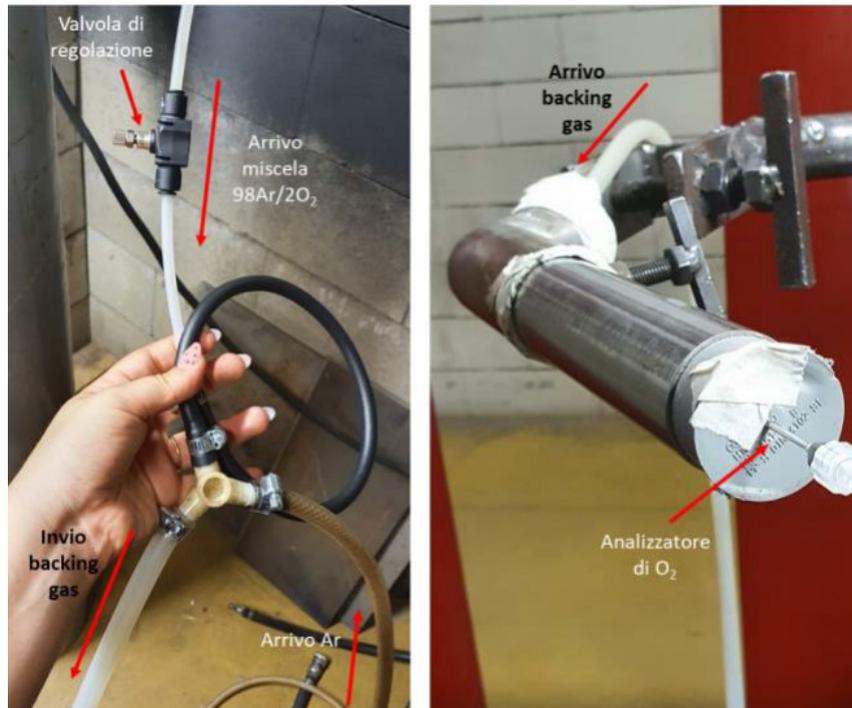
Setup di saldatura e regolazione della concentrazione di ossigeno a rovescio - welding setup and control of the oxygen concentration in the backing gas.
